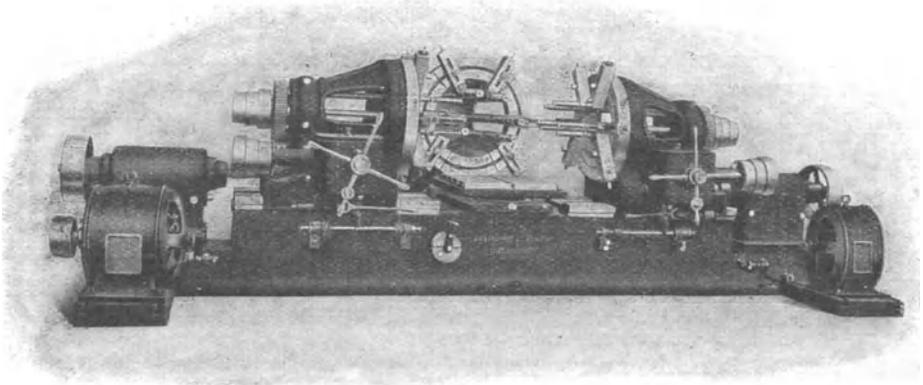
Mehrspindelige Wagerecht-Bohrmaschine.
